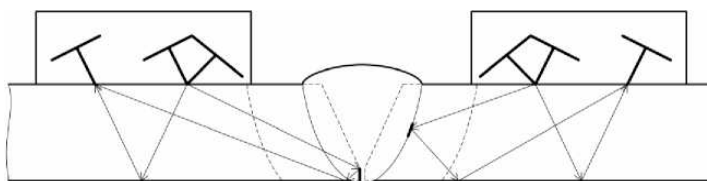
Схема контроля стыковых сварных соединений специализированным преобразователем СП5-75КУБ
